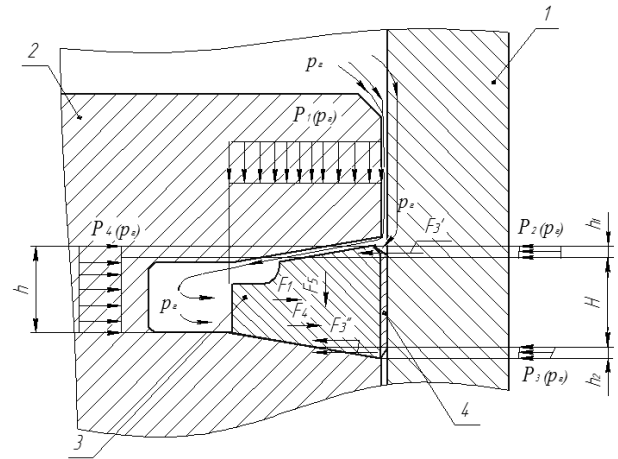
Принципиальная схема действия нагрузок на поверхности верхнего компрессионного кольца с цилиндрической беговой поверхностью при рабочем такте двигателя КамАЗ 740.354-450:
